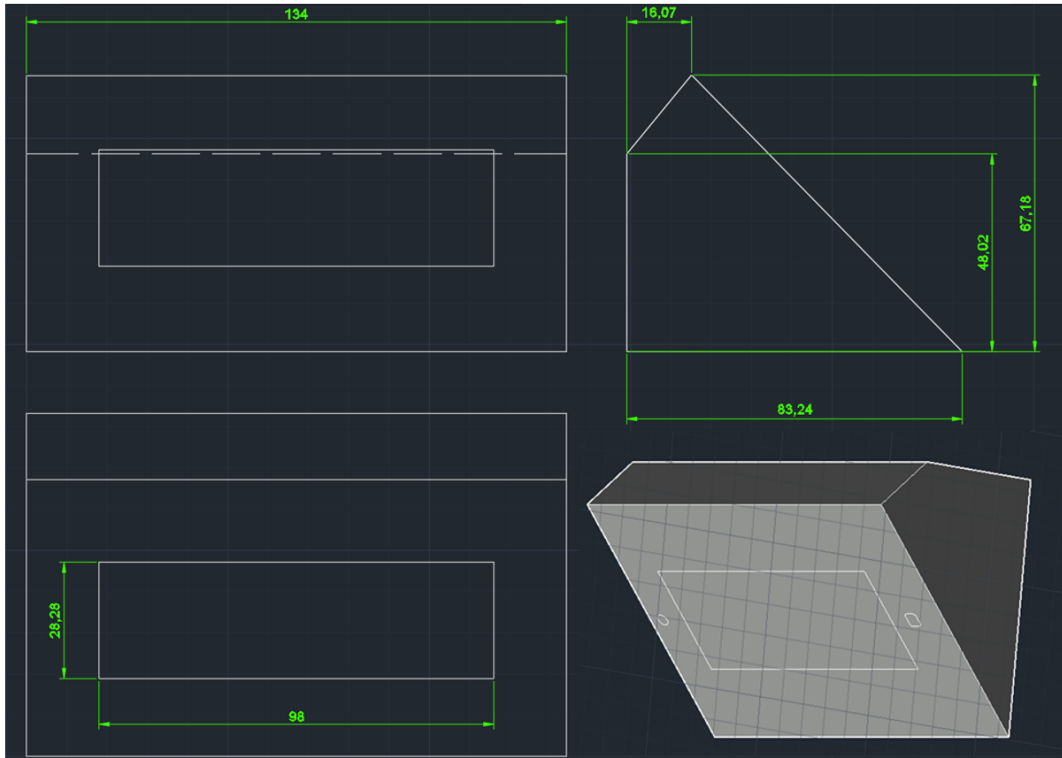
Diseño de la carcasa del dispositivo. Fuente [Autor]
